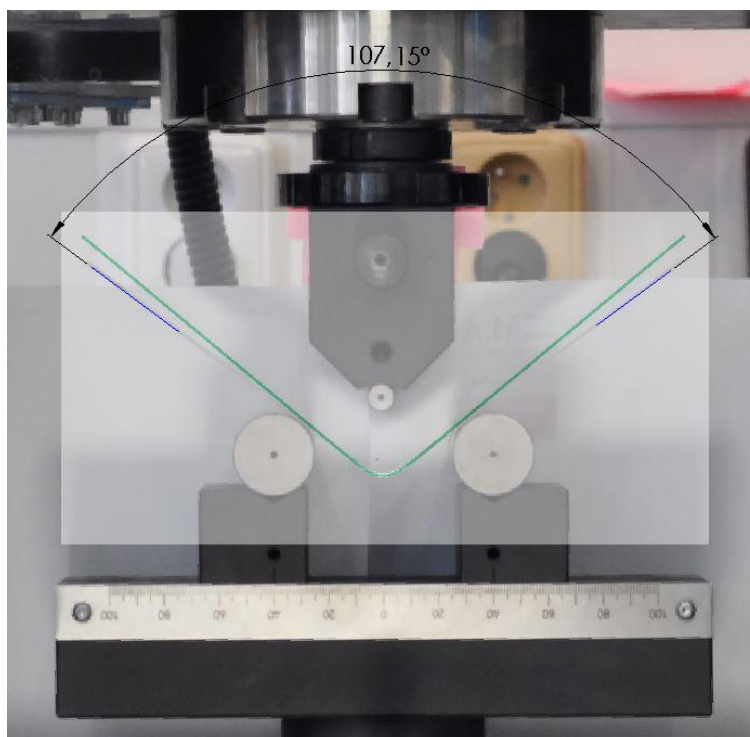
Zatížený stav - porovnání vzorku tloušťky 0,6 mm - podpory 160 mm
